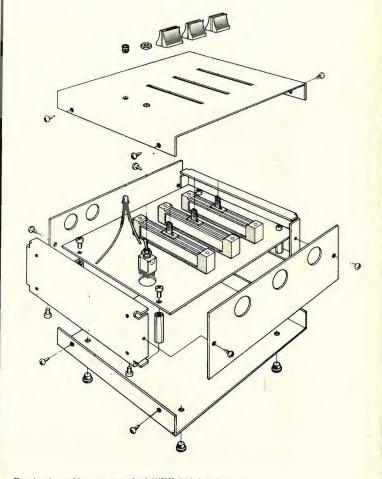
Assemblaggio generale dell'UK 716 dell'Amtron.
